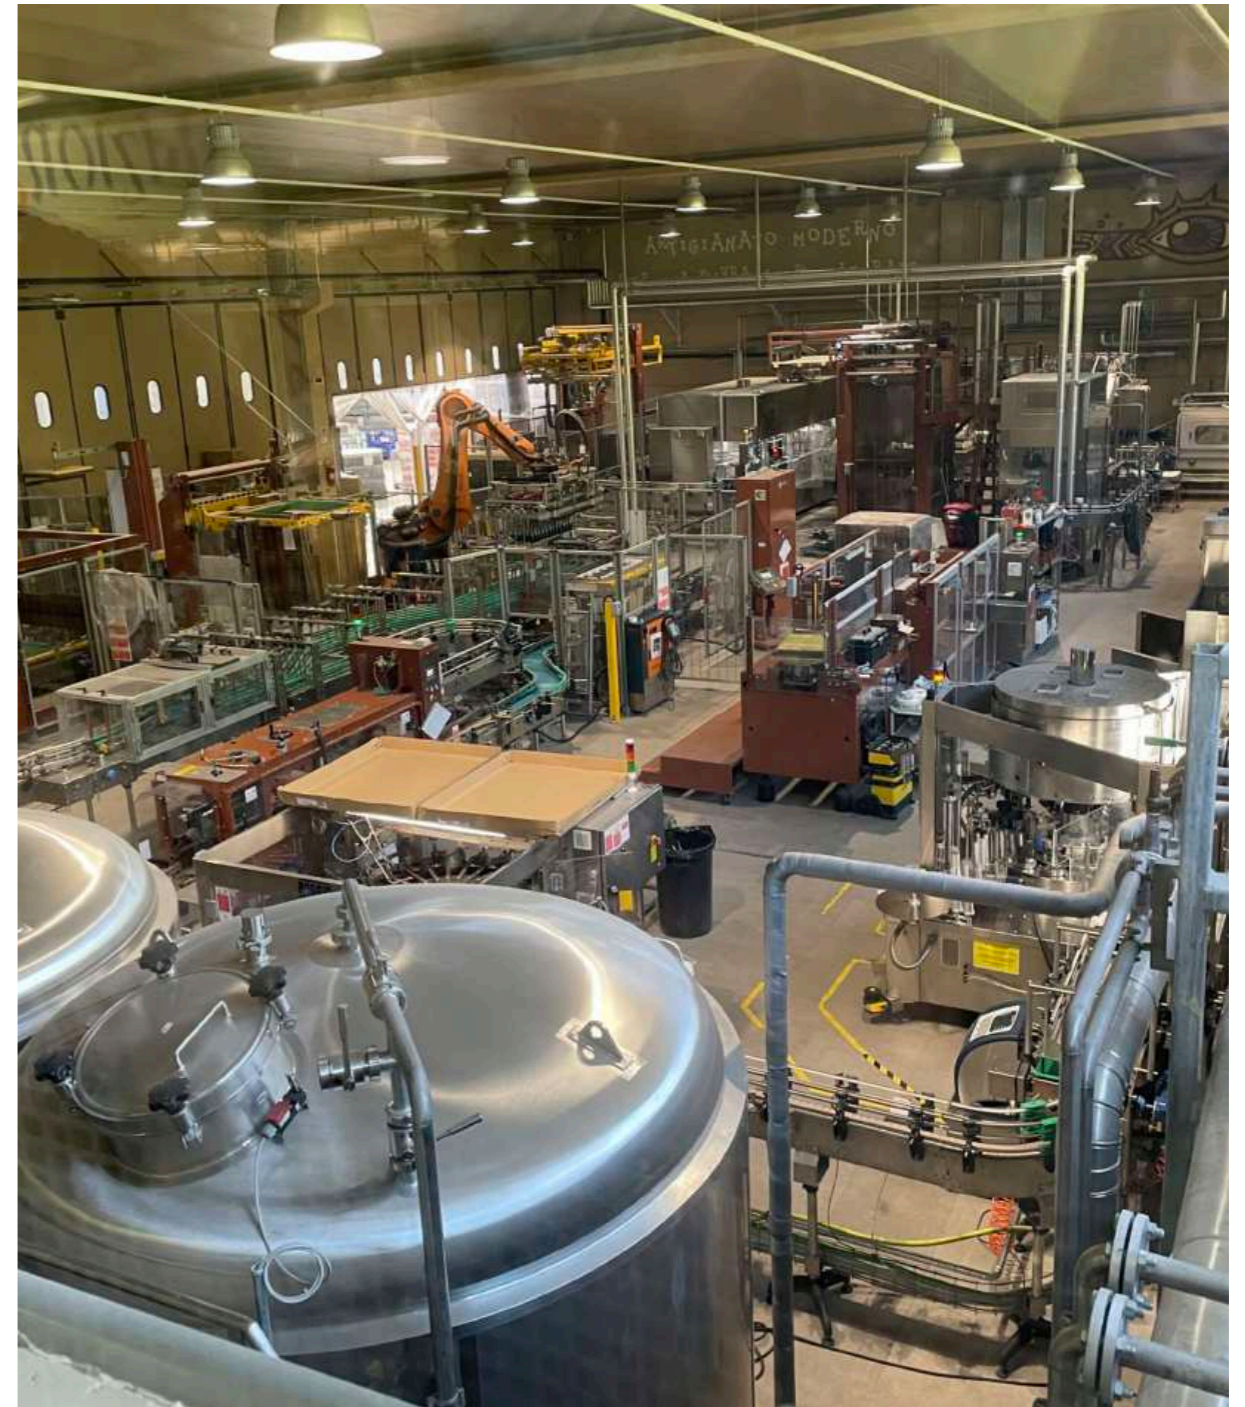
Impianto di stoccaggio ed etichettatura. Fonte: foto dell'autore
